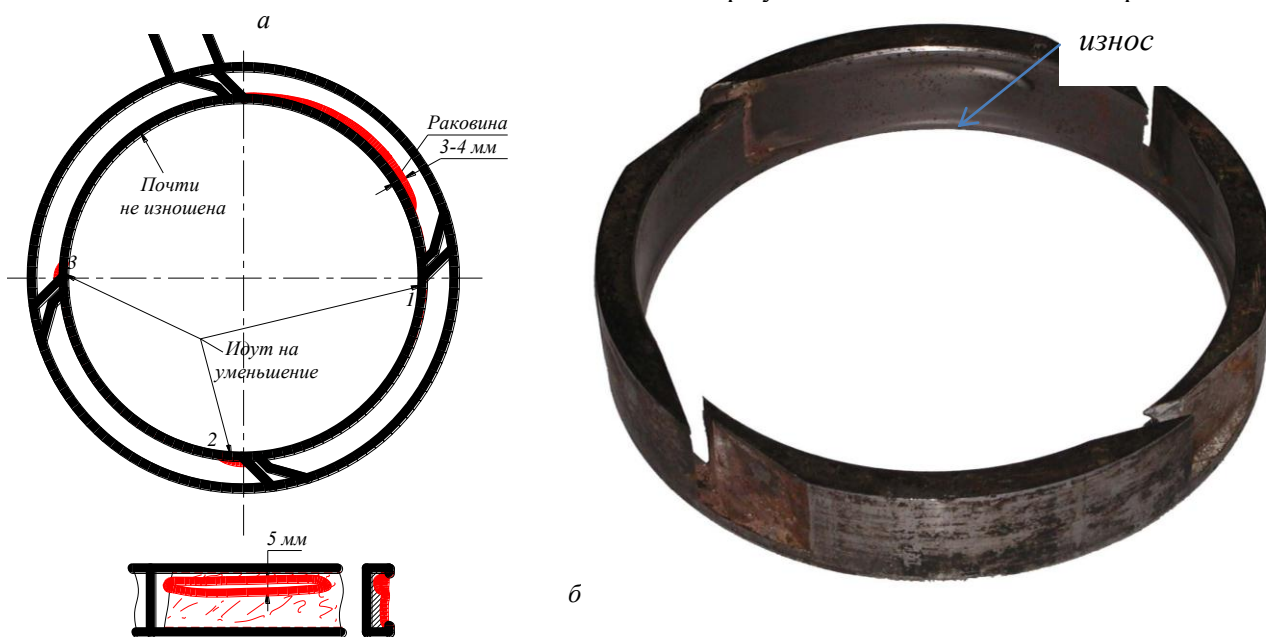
Футеровка камеры измельчения вихре-акустического диспергатора: а – фотография футеровки; б – схема газообразивного изнашивания футеровки
